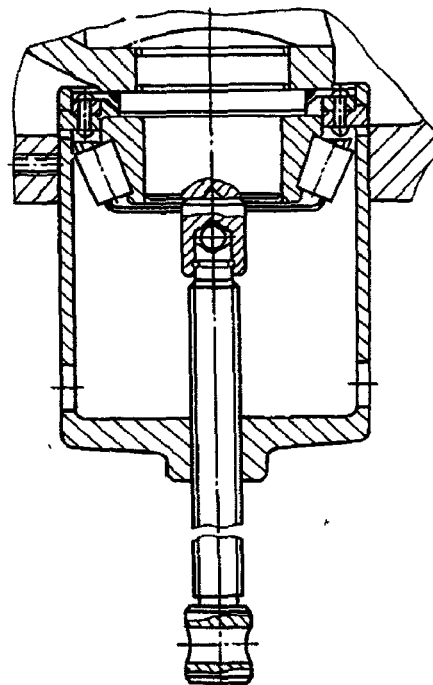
Выпрессовка подшипника шкворня переднего моста
